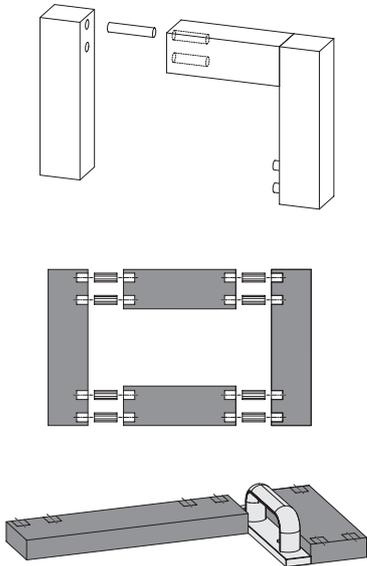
Ensamblaje de marcos por clavijas a 90°
